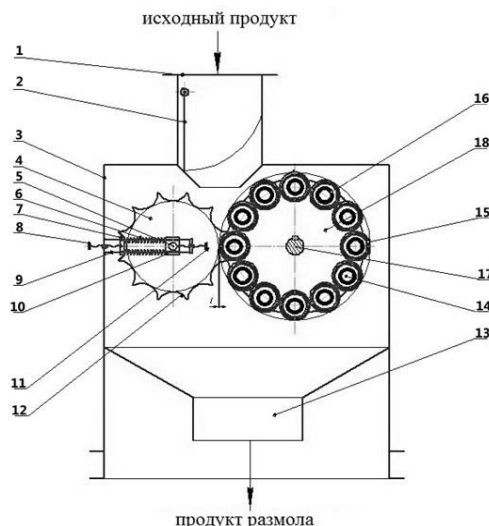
Общий вид зубчато-роликового измельчителя для зерна
